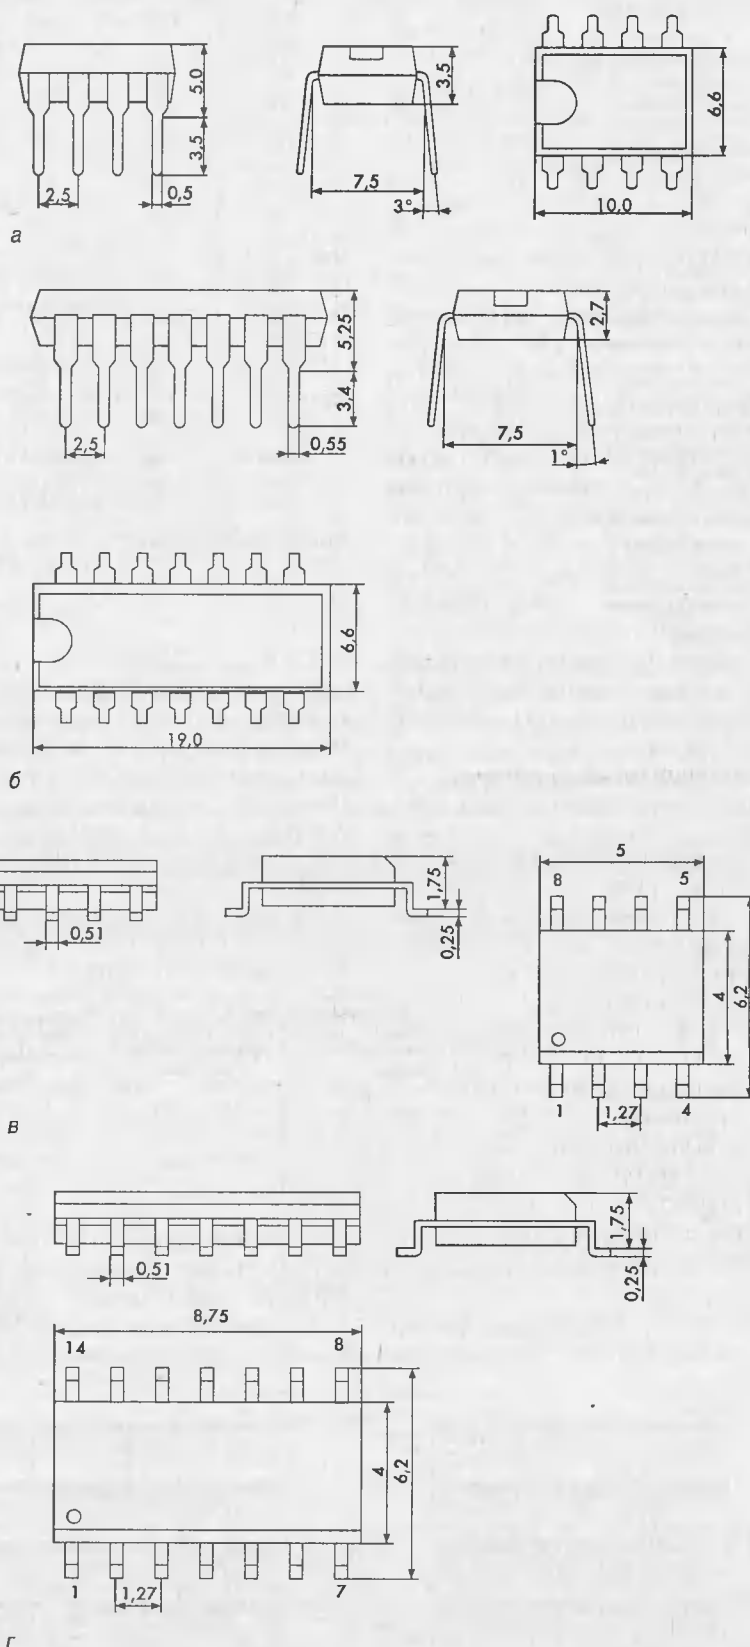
а — корпус 2101.8-1, б — корпус 201.14-2, в — корпус 4303Ю.8-А, г — корпус 4306.14-2.
